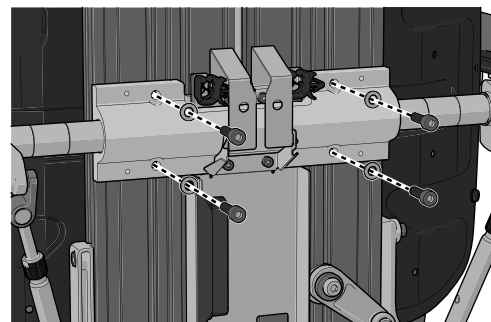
Die Armlehnen sind mit vier Schrauben befestigt.
